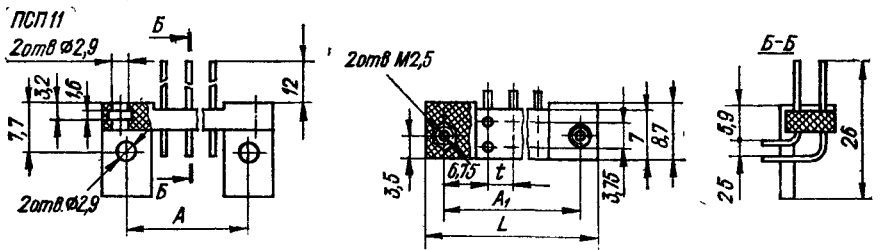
Конструктивные размеры плат ПСП11 — ПСП13 и разметки для их крепления
